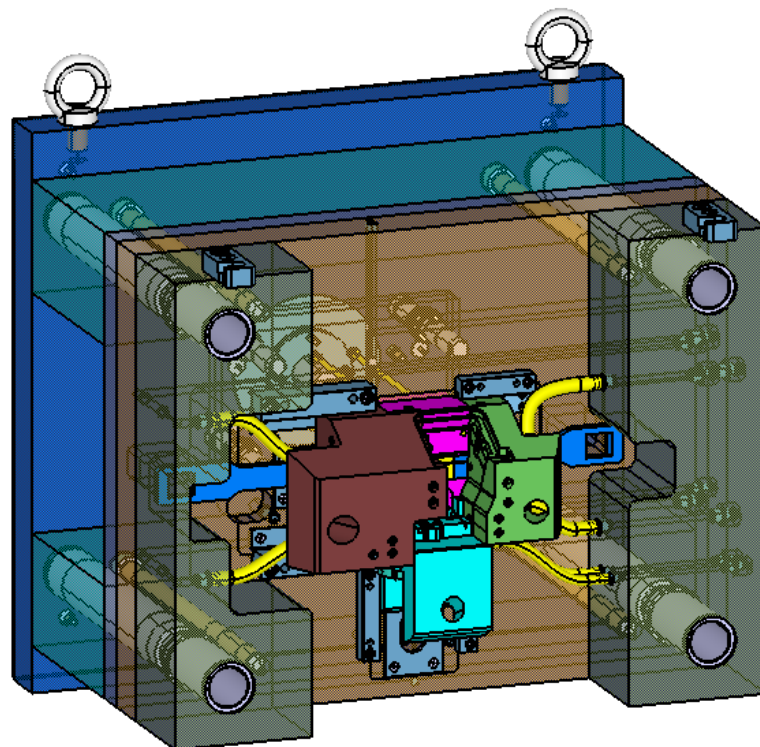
Zajištění formy HASCO Z73/20x32x80 [14]
